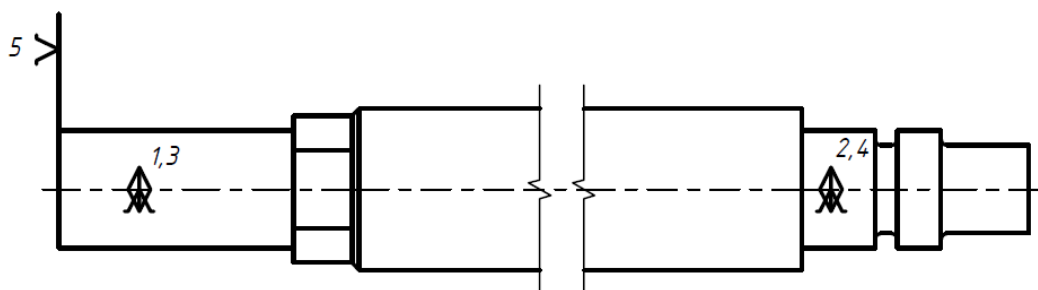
Схема базування при обробці циліндричної поверхні штока.
